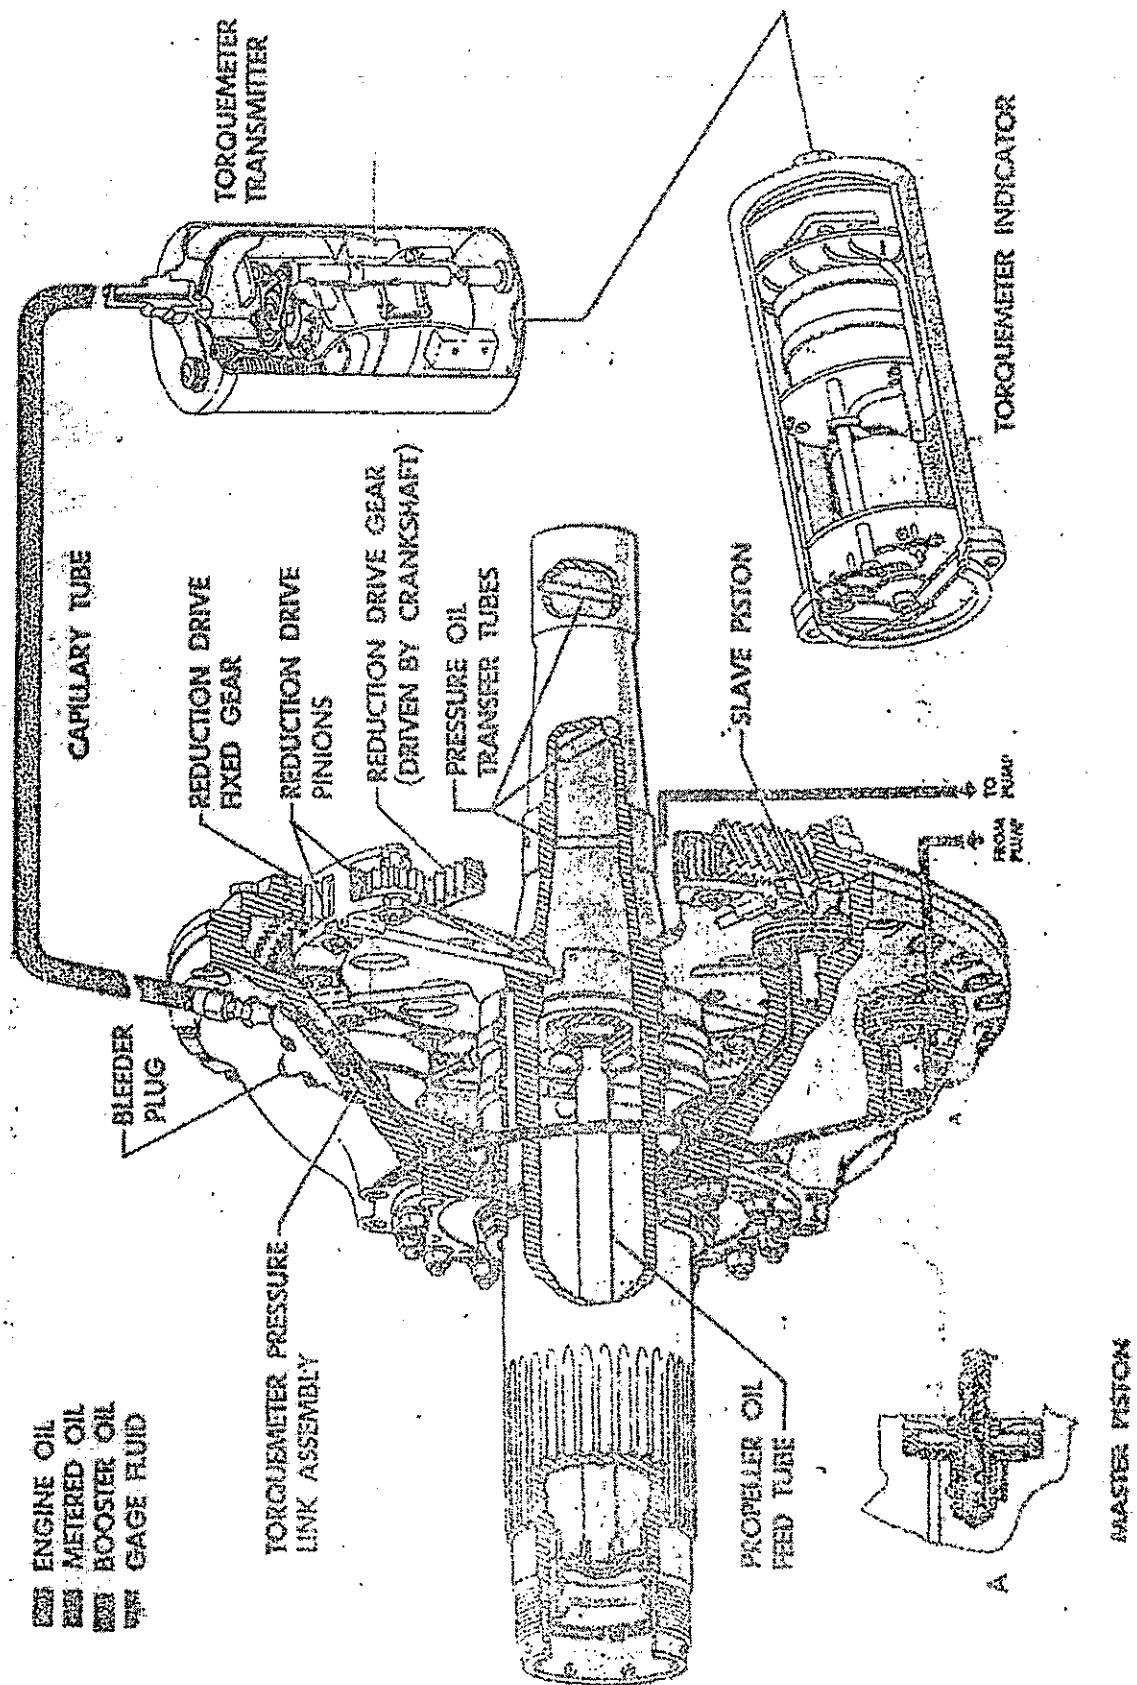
PLANETARY GEAR (19)
